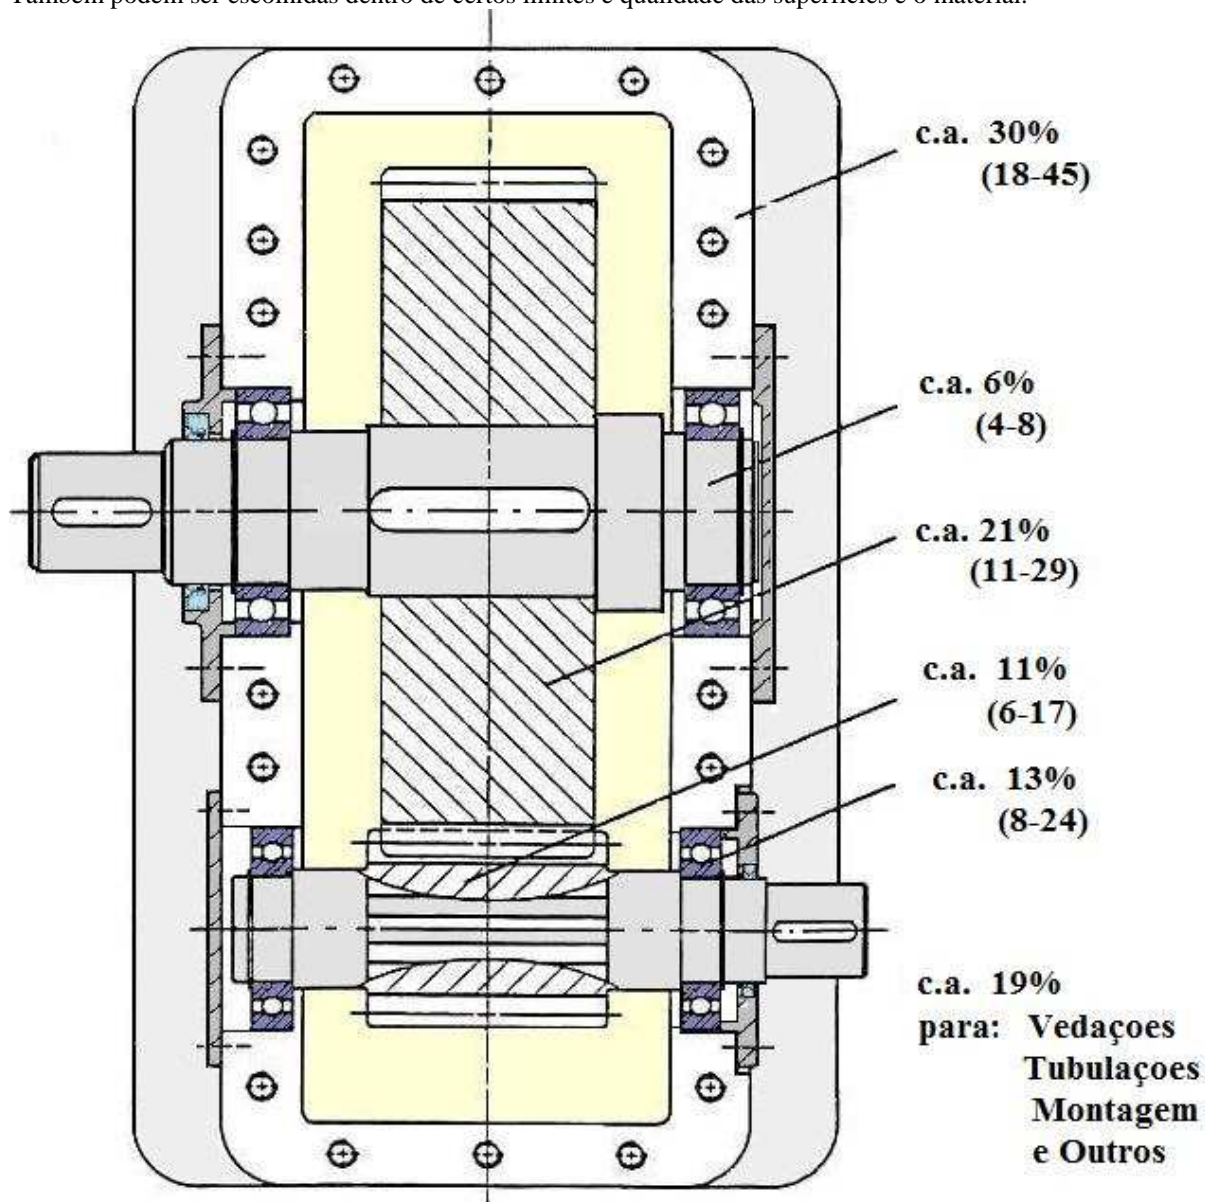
Estruturação de custos de um redutor com engrenagens cilíndricas retas com capacidade de 700 CV (baseado em informações de diferentes fabricantes)
